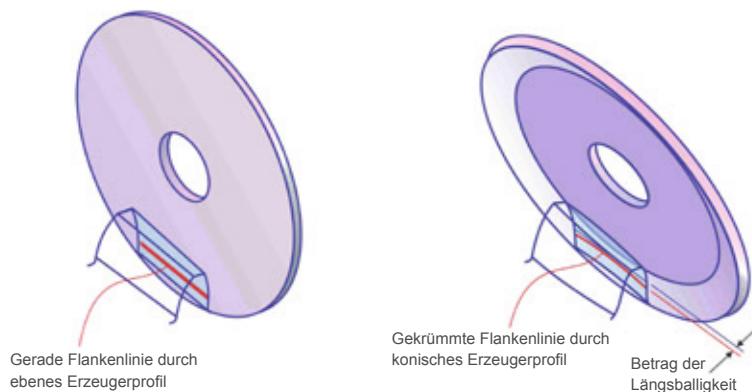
Längsballigkeits-Erzeugung mittels tellerförmigen Werkzeugen.
